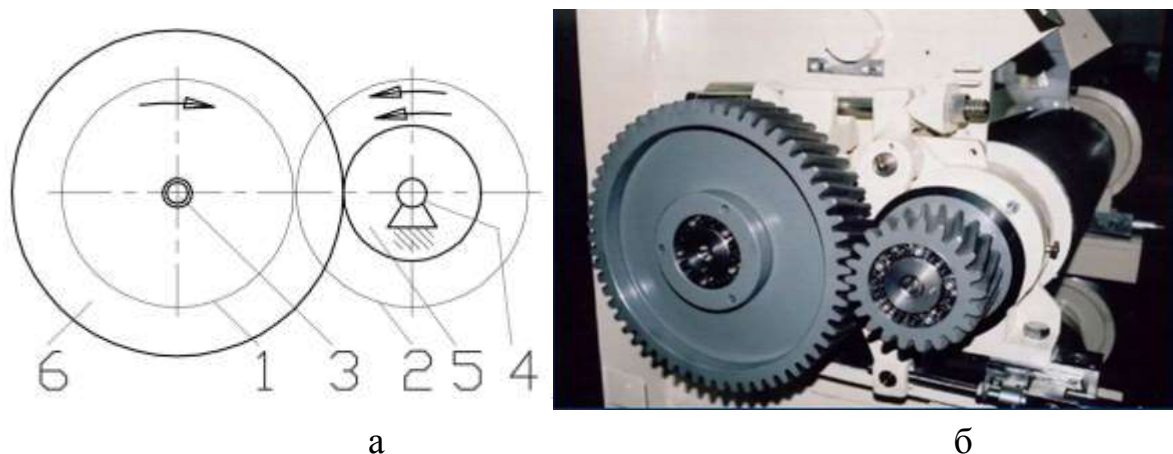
Міжвальцьова передача: а) схема б) косозубі зубчасті колеса міжвальцьової передачі.
